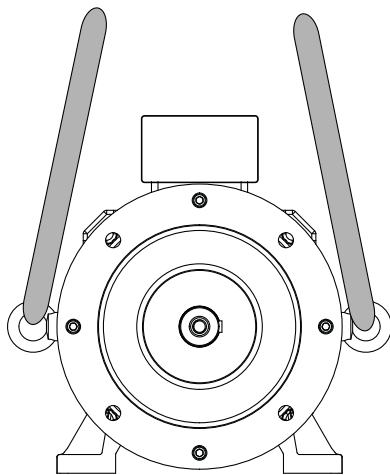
Транспортировка двигателя с двумя рым-болтами по бокам корпуса двигателя
